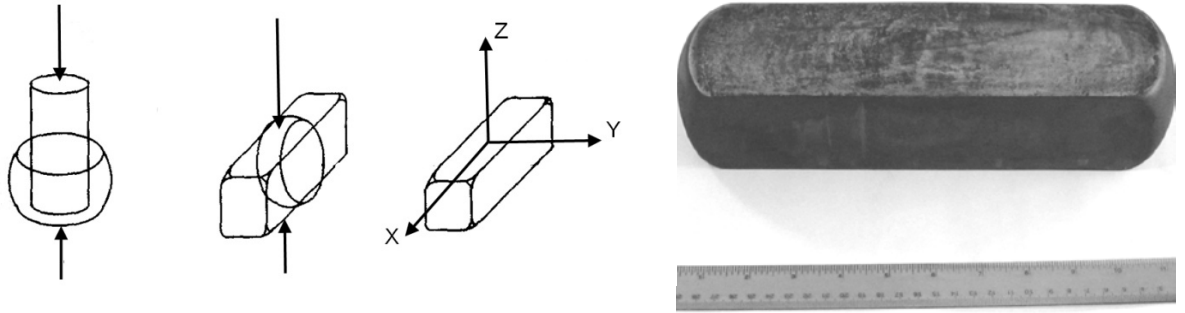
Схема обработки всесторонней изотермической ковкой (ВИК), направления осей деформации и внешний вид обработанной заготовки сплава ZK60
